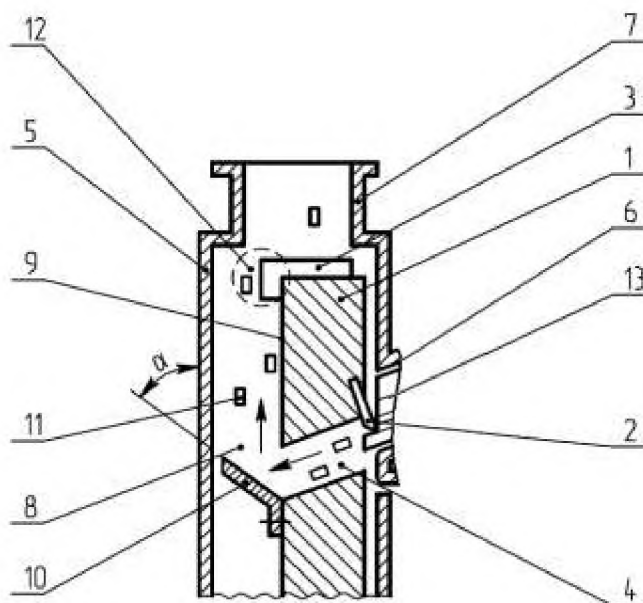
Принципова схема утворення тріски в розроблюваному дисковому подрібнювачі: 1-диск; 2- ніж; 3- лопатка; 4- ножовий отвір; 5- кожух; 6- завантажувальна камера(патрон); 7- вивідна горловина; 8- задня стінка ;9- задня площина 10- криволінійна пластина; 11- тріска; 12- зона захоплення; 13- деревина
